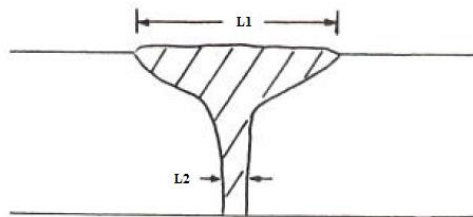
Configuración del cordón de soldadura [2].
